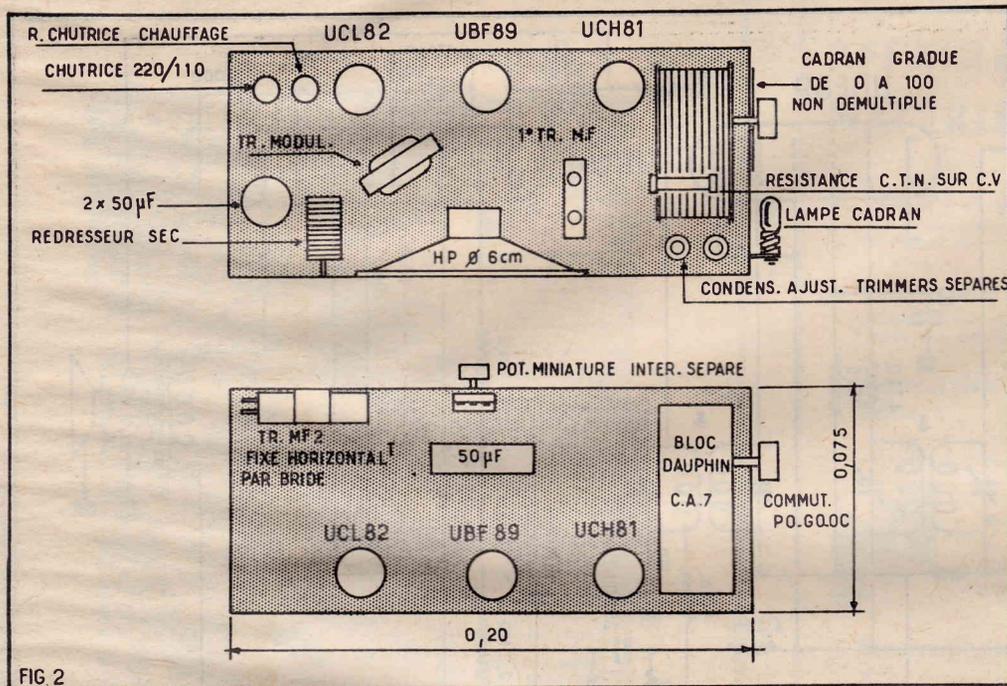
En haut : Vue dessus. En bas : Vue dessous.
